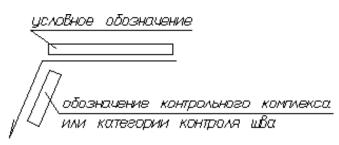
Обозначение контрольного комплекса или категории контроля шва
